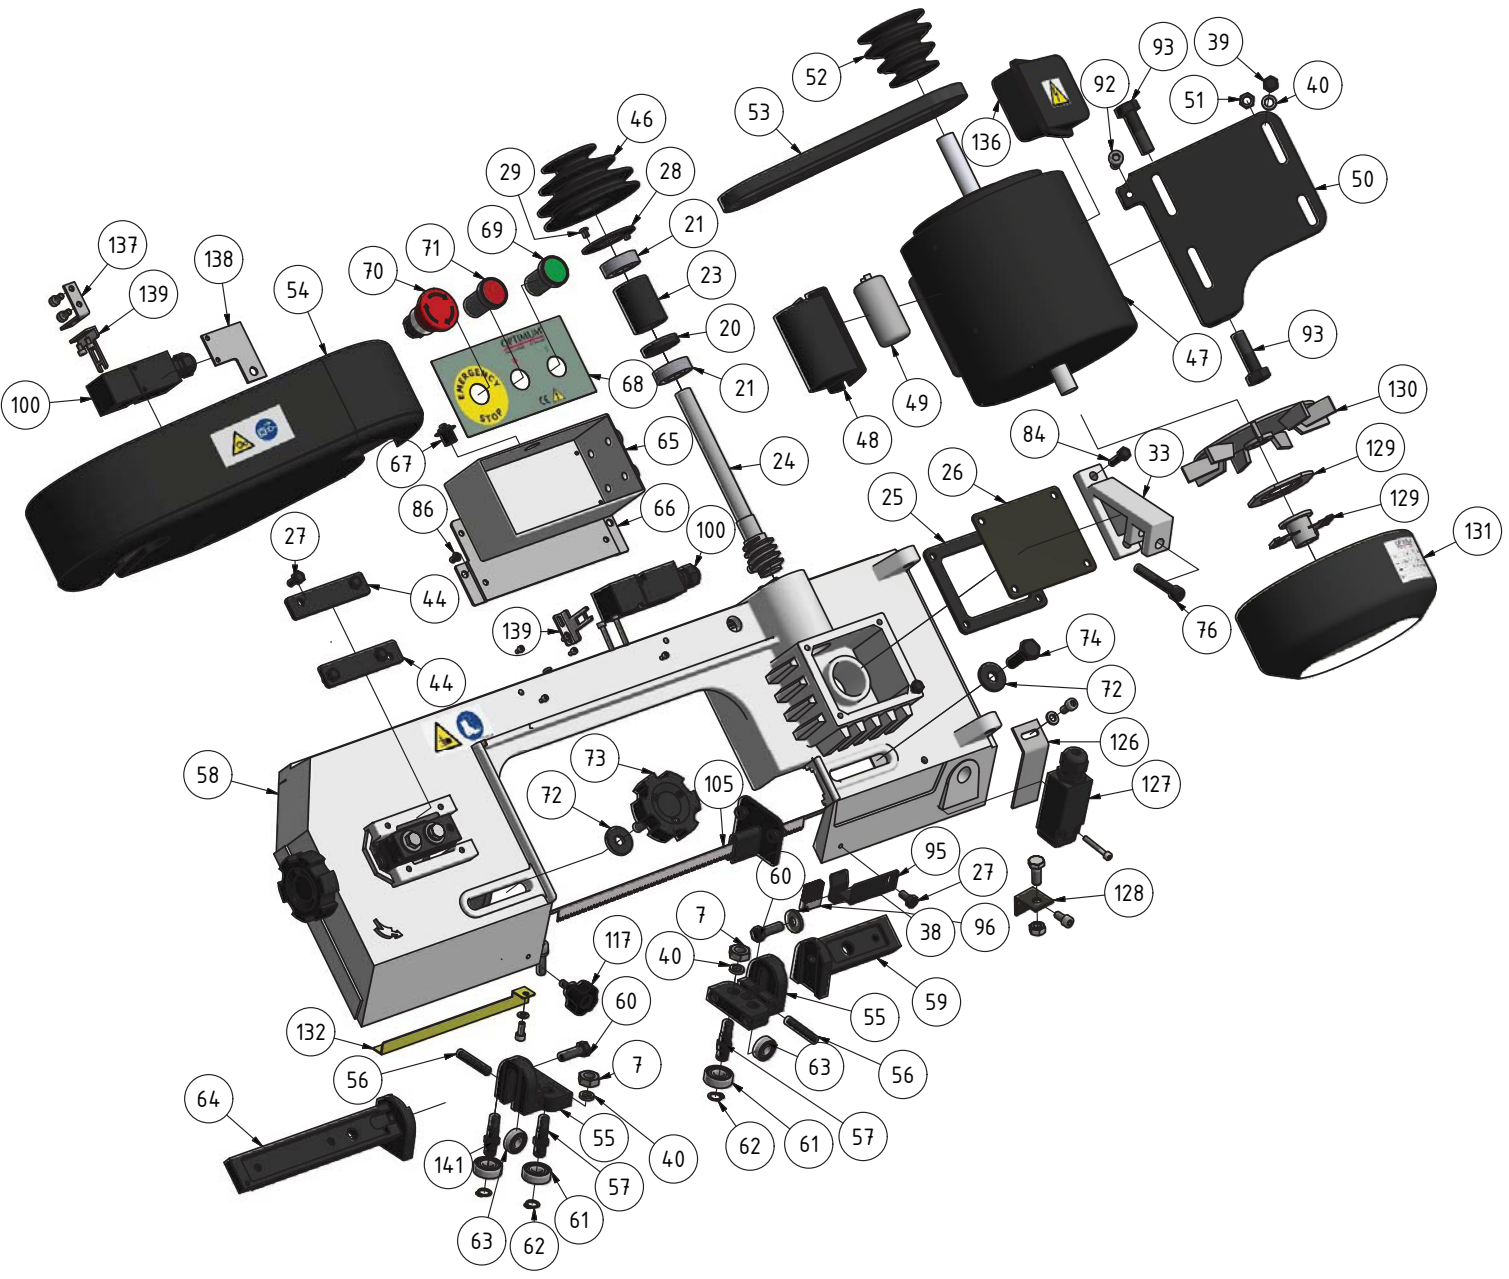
Ersatzteilzeichnung 1 von 4 - Parts drawing 1 of 4
